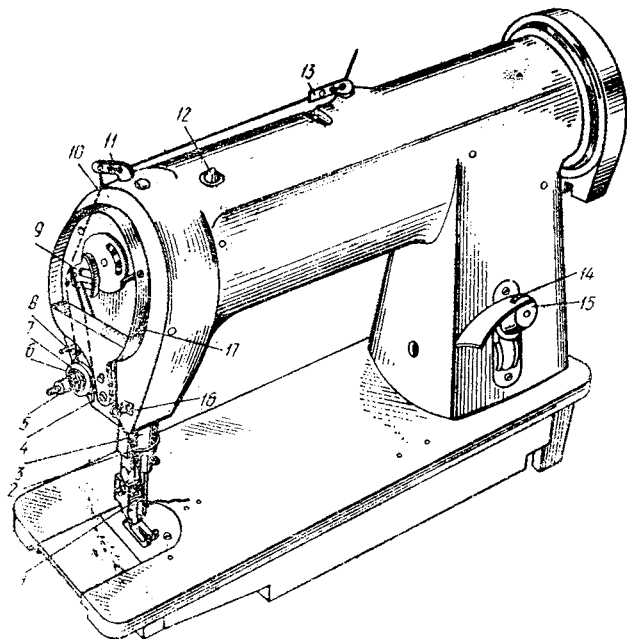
Внешний вид машины 97-А кл. и заправка верхней нитки
